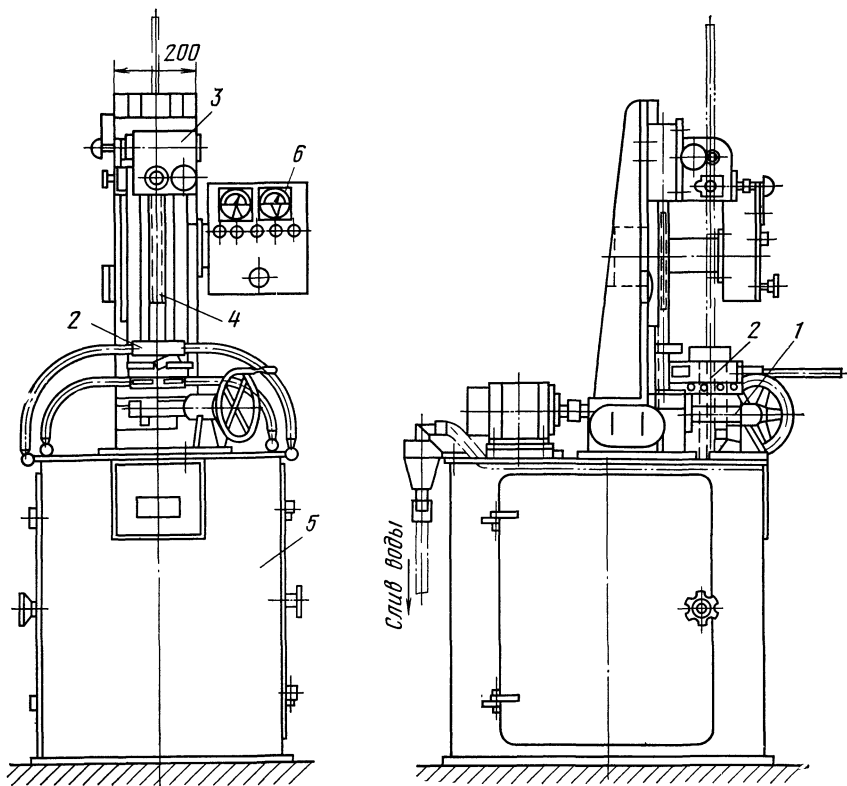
Аппарат А-578М для электрошлаковой наплавки
